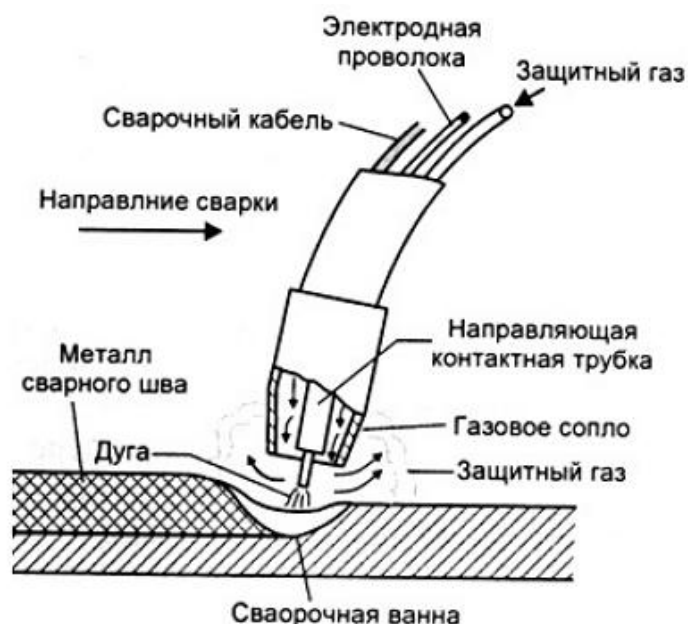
Механизированная сварка в среде защитного газа
